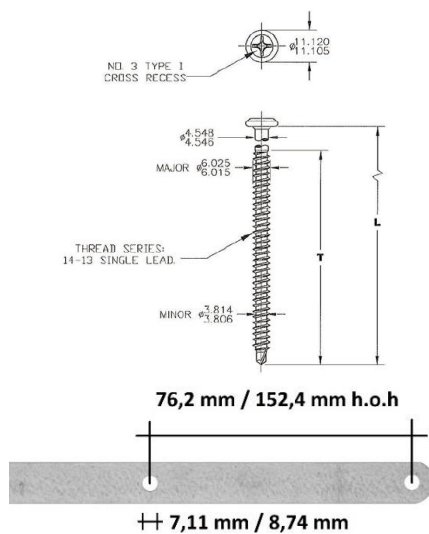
Schroef Firestone "ALL PURPOSE FASTENER" + bevestigingsstrip Firestone "Metal Batten Strip"
